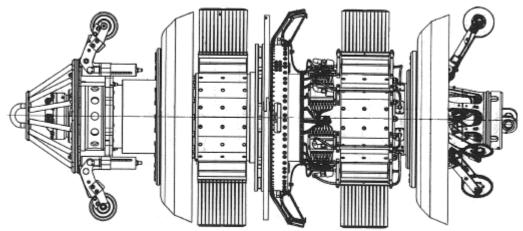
Чертеж общего вида дефектоскопа внутритрубного магнитного 42-MCK.01-00.000-01 и 48-MCK.01-00.000-01
